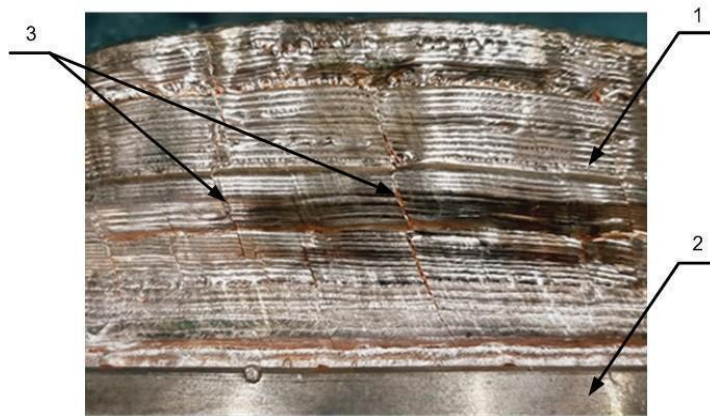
Стенка наружного стакана с трещинами: 1 – заготовка основания;
